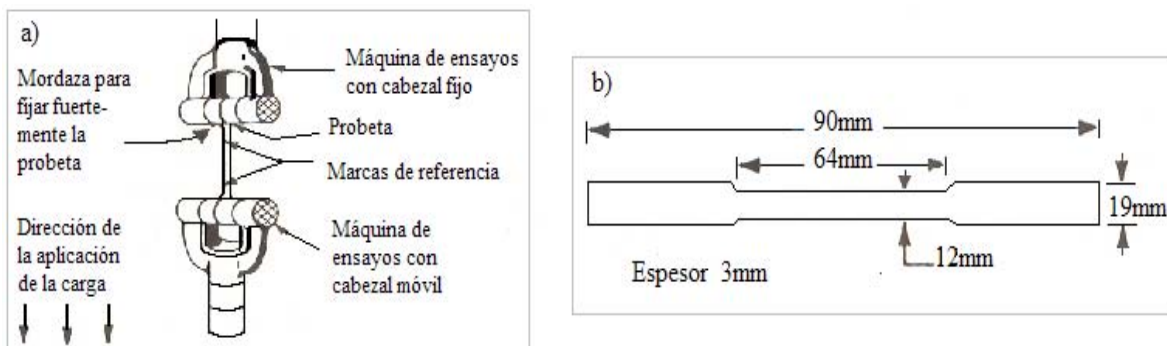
a) Ensayo de tensión, b) dimensiones de la probeta
